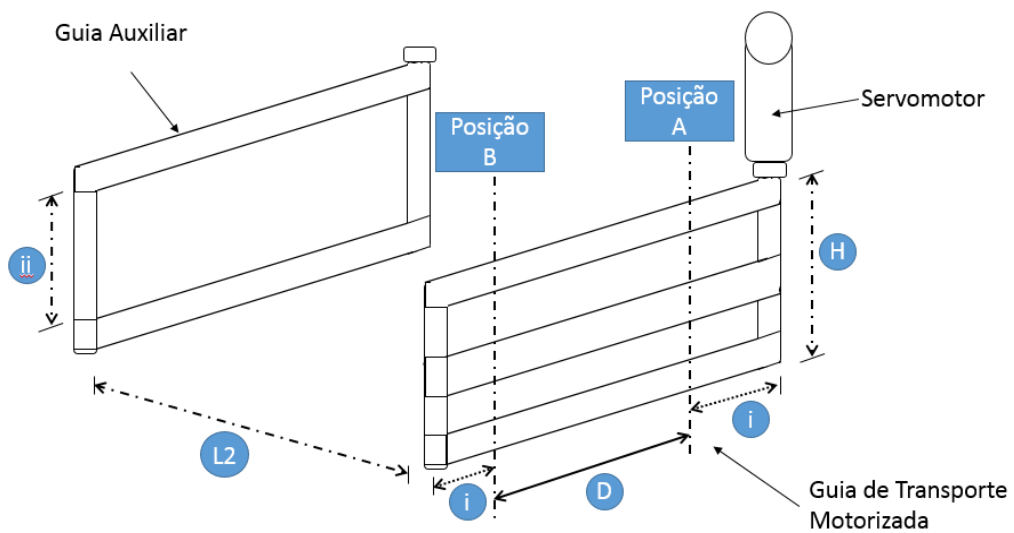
Dimensões da Guia Auxiliar e GTM
